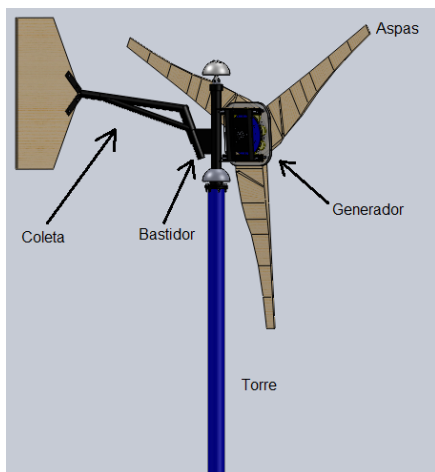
Armado completo de rotor, estator, aspas y coleta.
